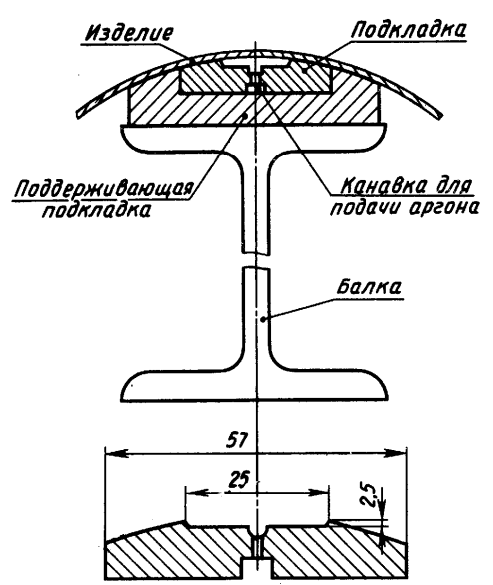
Конструкция подкладки для сварки продольных швов тонколистовых оболочек
